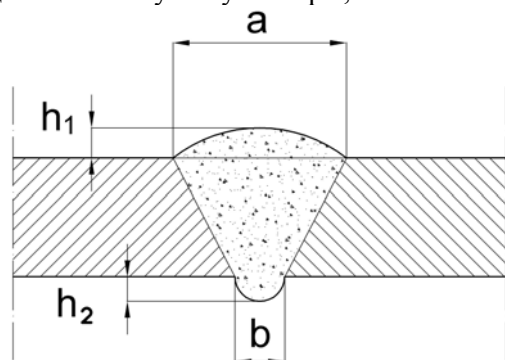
Схема основных геометрических размеров сварного шва
